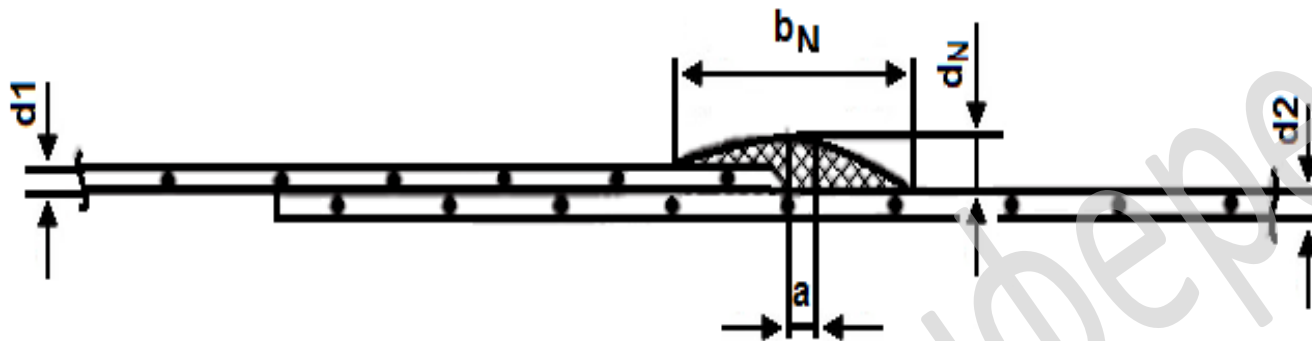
Форма и размеры сварного шва при экструзионной сварке
